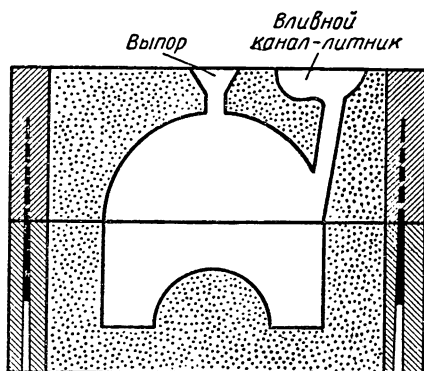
Вертикальный разрез готовой для заливки земляной формы.
